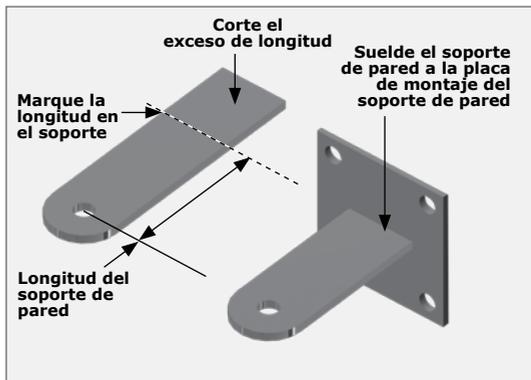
CORTE Y SUELDE EL SOPORTE DE PARED
